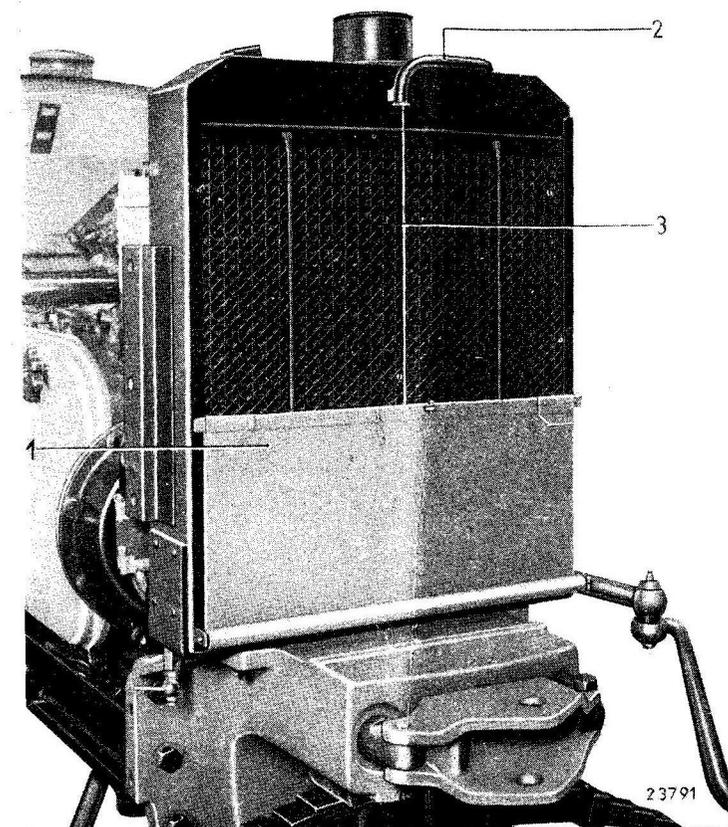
Bloc de radiateur avec rideau après le démontage du couvre-radiateur
